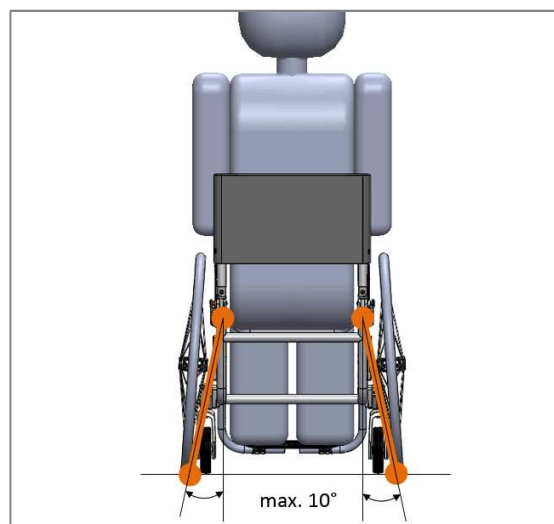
Andamento dei retrattori posteriormente con angolazione di ancoraggio massima e punti di collegamento (vista posteriore)
